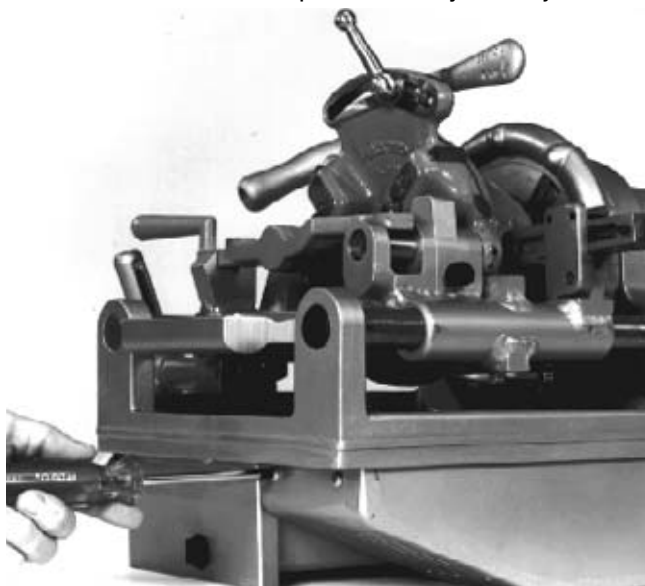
Afloje y extraiga los tornillos de la tapa del motor
